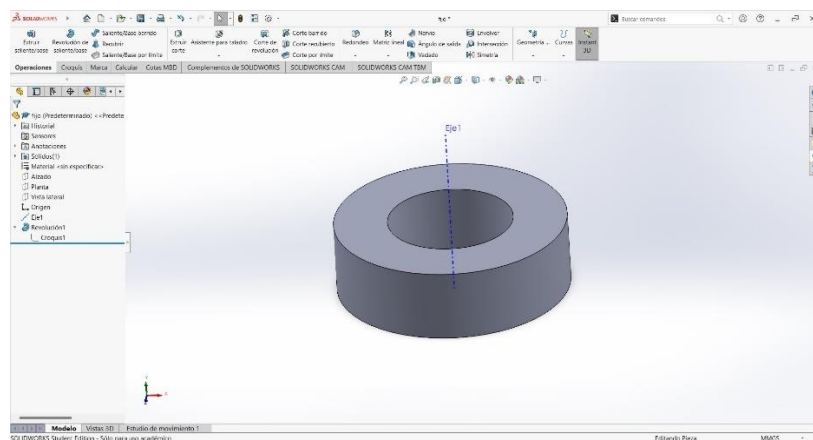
Resultado final de la pieza de guía. Fuente: SolidWorks
